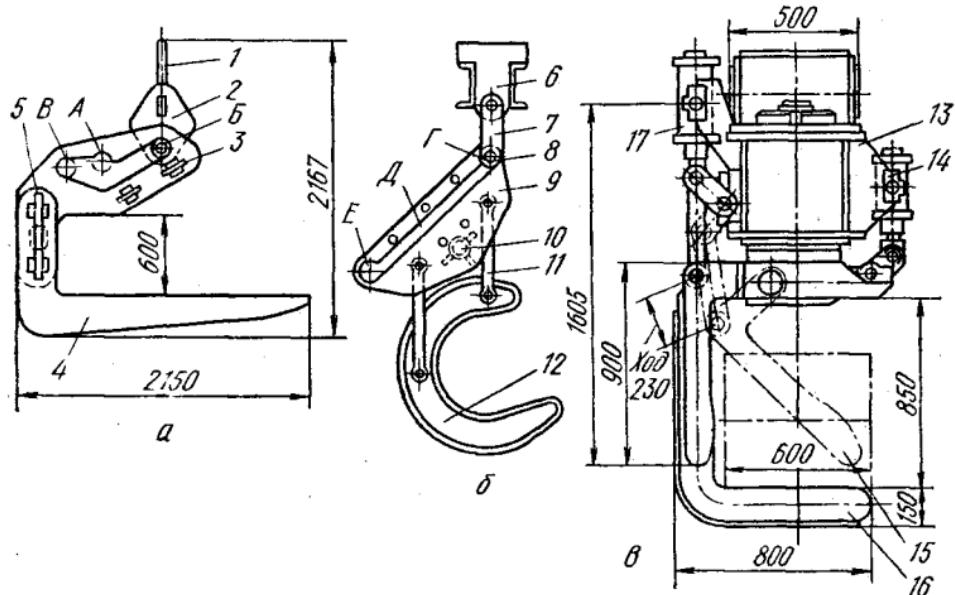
Грузозахватные вилочные устройства для транспортирования металла:
